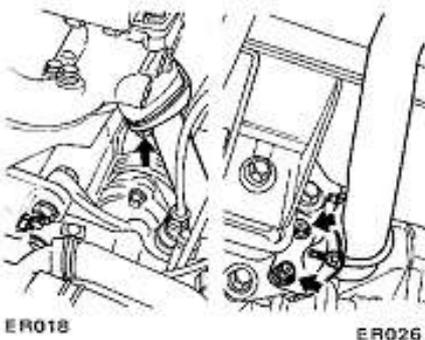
Débranchement de la section avant du tuyau d'échappement
